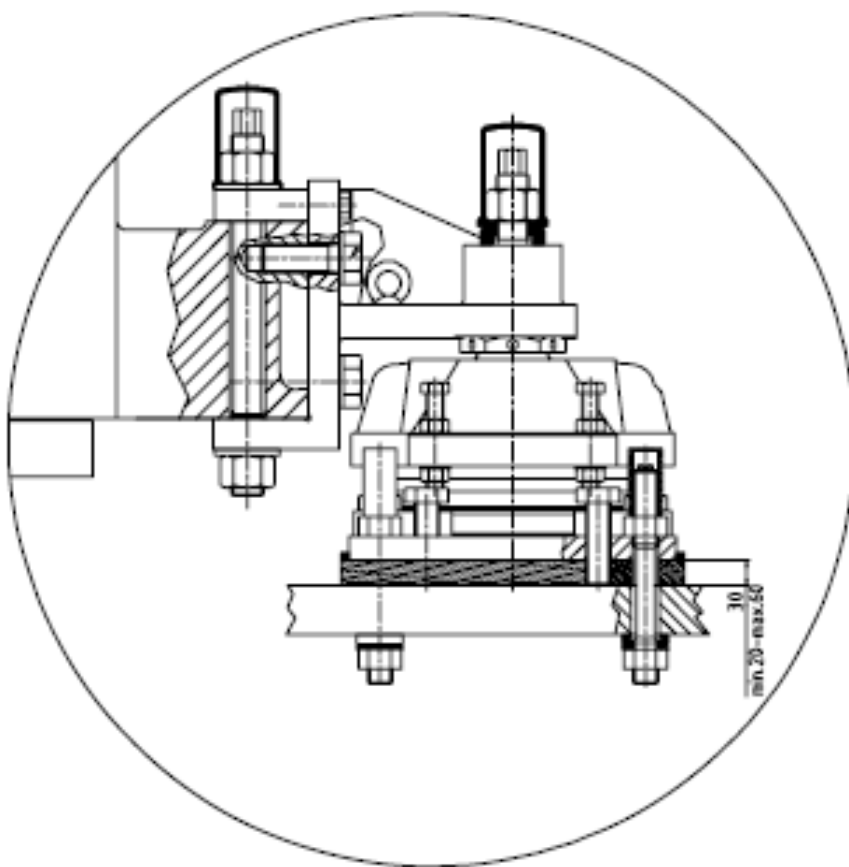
Кріплення двигуна до суднового фундаменту
